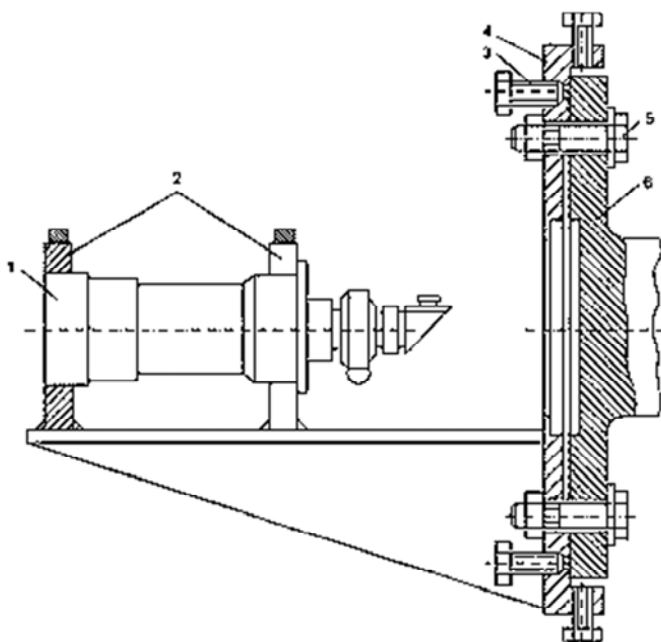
Схема крепления визирной трубы на фланце вала:
